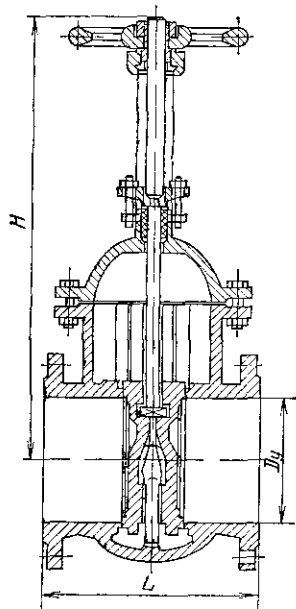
Задвижка параллельная фланцевая с выдвижным шпинделем 30ч6бр
